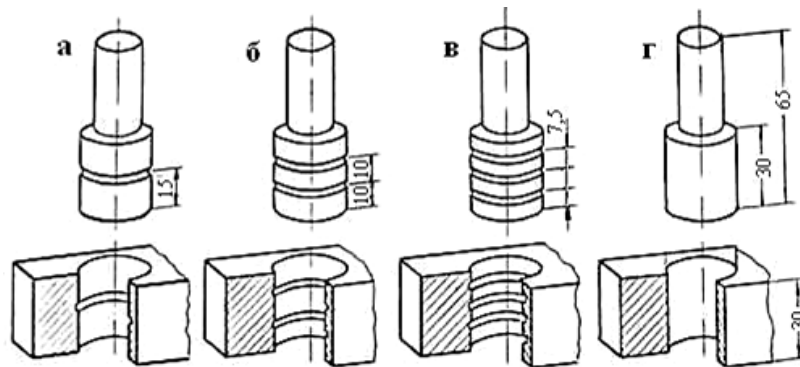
Геометрические размеры опытных образцов направляющих элементов: а – с одной канавкой; б – с двумя канавками; в – с тремя канавками; г – без канавок
